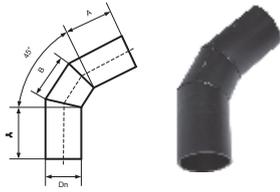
Отвод 45° сварной 3-х сегментный
